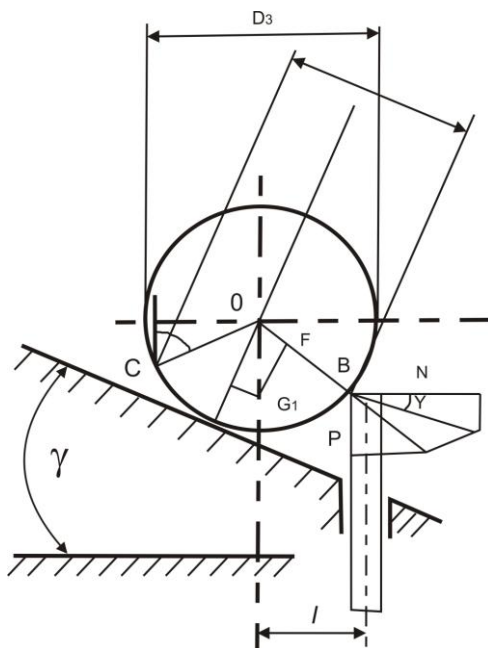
Схема усилий, действующих на отсекатель механизма поштучной выдачи деталей
